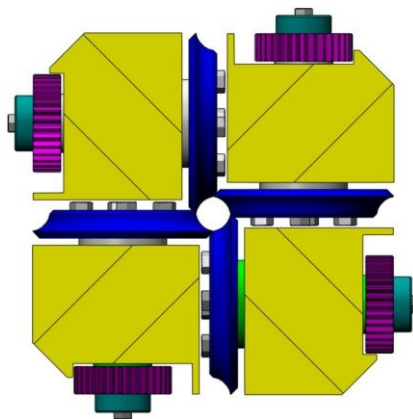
Схема установки подушек валков при формировании круглого четырехвалкового калибра
